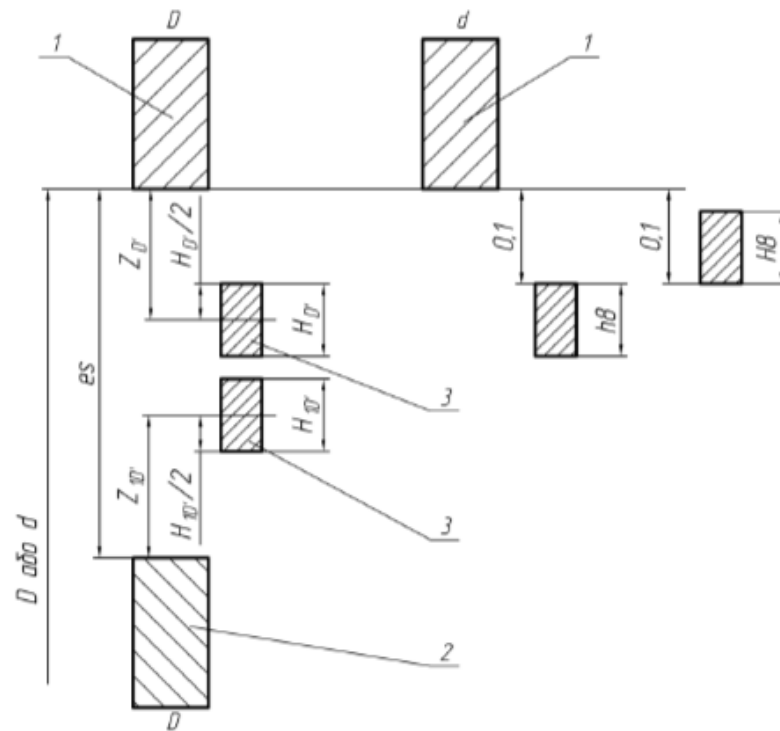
Схеми полів допусків калібра-пробки та калібра-кільця за нецентруючими діаметрами: 1 – поле допуску нецентруючого діаметра d або D втулки; 2 – поле допуску нецентруючого діаметра D вала; 3 – поле допуску на виготовлення калібра-пробки і калібра-кільця ; $h8$ – поле допуску внутрішнього діаметра d_k калібра-пробки; $H8$ – поле допуску d_k калібра-кільця [22].
